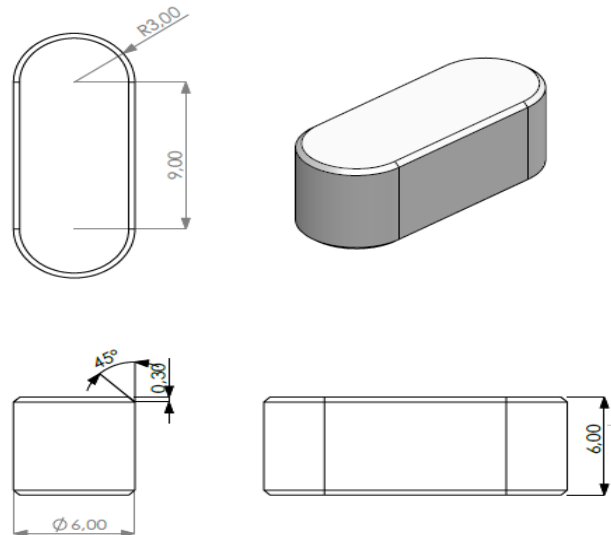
Vista alámbrica e isométrica chaveta 6x6 [mm].
